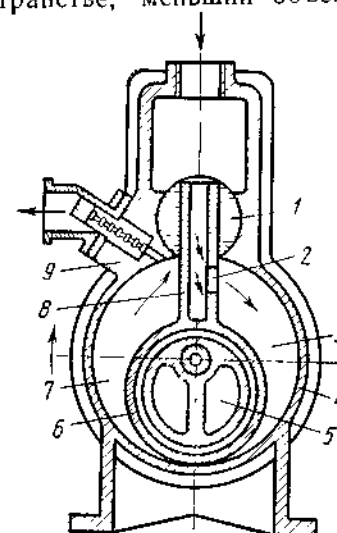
Устройство золотникового насоса: 1 — шаровая опора, 2 — всасывающее отверстие, 3 — камера всасывания, 4 — корпус, 5 — эксцентрик, 6 — обойма, 7 — камера сжатия, 8 — патрубок, 9 — выпускной клапан
